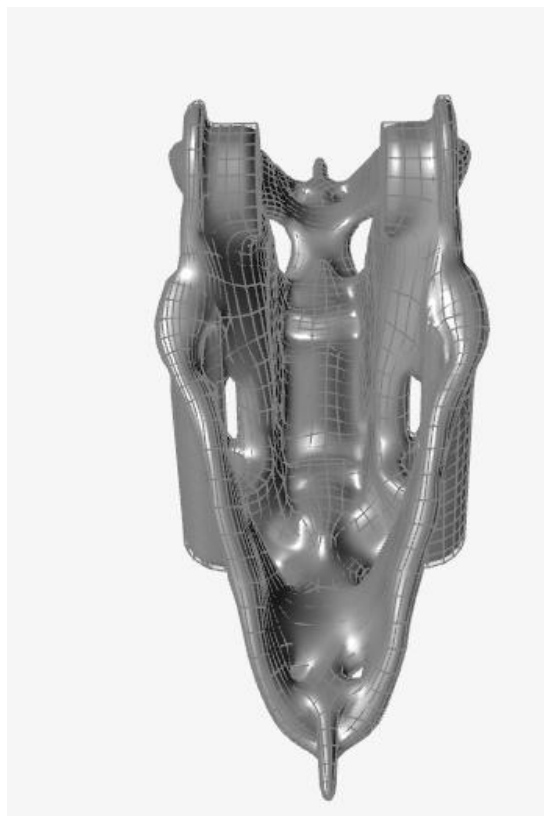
Detalle refinamiento (3). Fuente: elaboración propia
